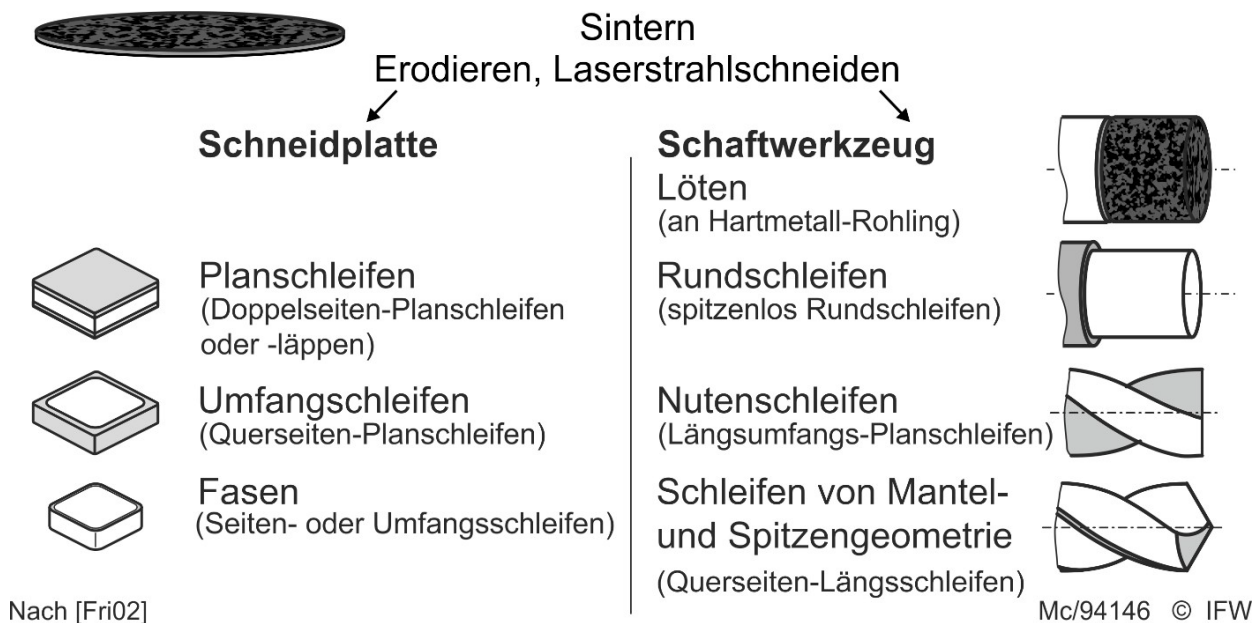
Prozessschritte der Schleifbearbeitung von PCBN-Zerspanungswerkzeugen
